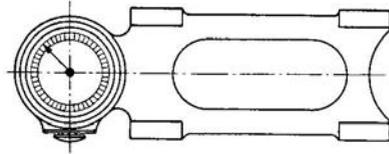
Einstellehre mit Meßuhr für Vorschubwalzen.
